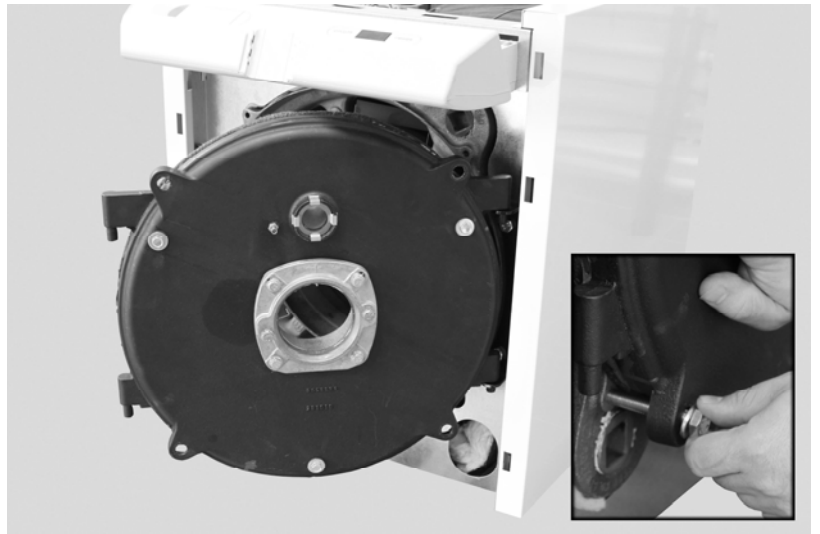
Kesseltür in Scharnierblech einhängen und mit den beiliegenden Schrauben am Kesselkörper fixieren.
